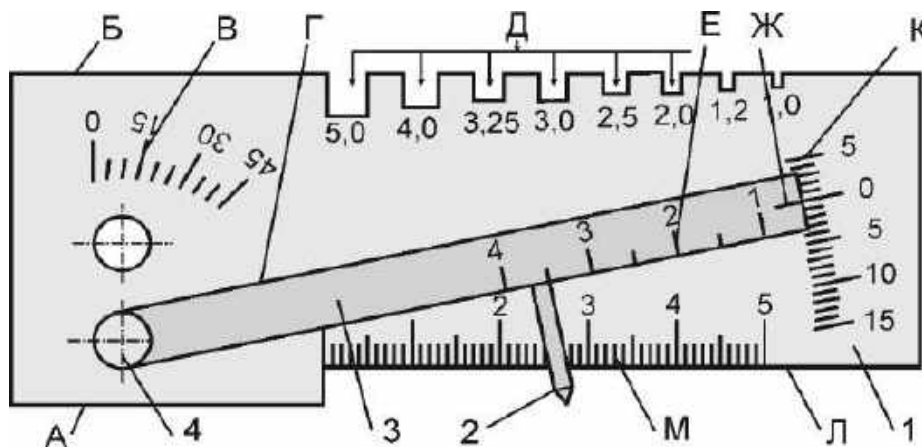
Універсальний шаблон зварника УШС-3:
